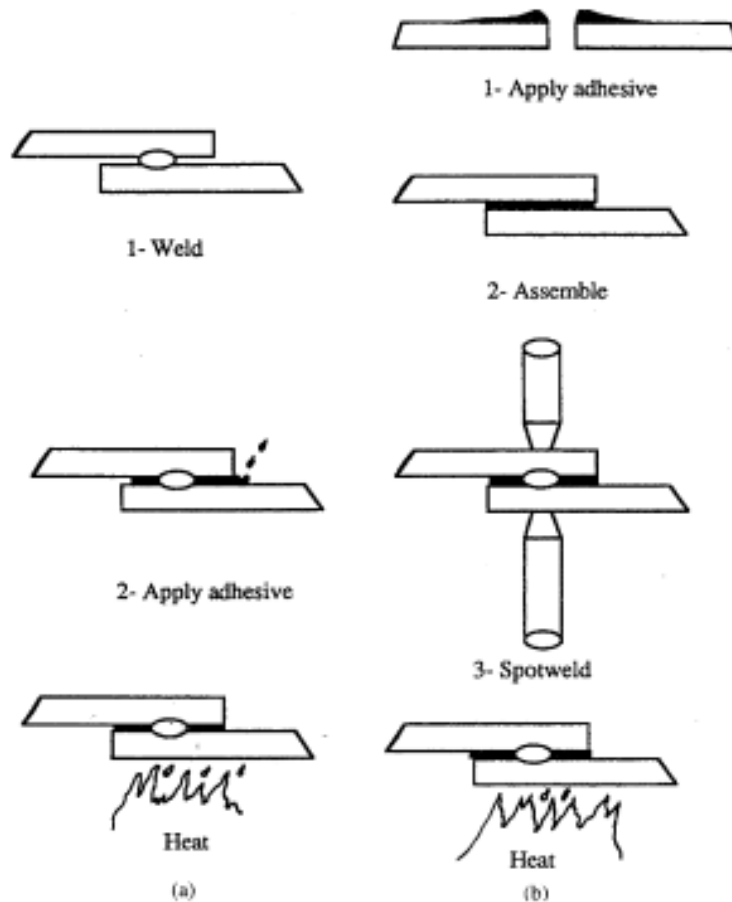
Técnicas de ligação adesiva soldada (a) *The flow-in technique* (b) *Weld-through technique* (da Silva 2011)
